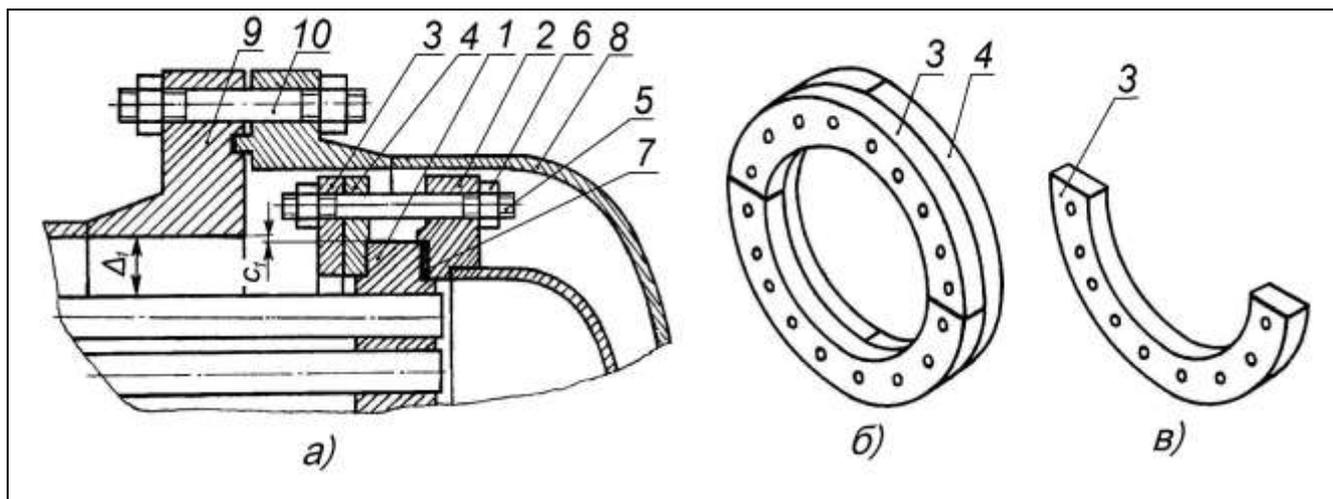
Плавающая головка типа П с двумя разрезными накладными фланцами 3 и 4: а) – общий вид; б) – взаимное положение разрезных фланцев 3 и 4 перед сборкой узла; в) – общий вид нижнего полукольца 3 до установки в аппарате
